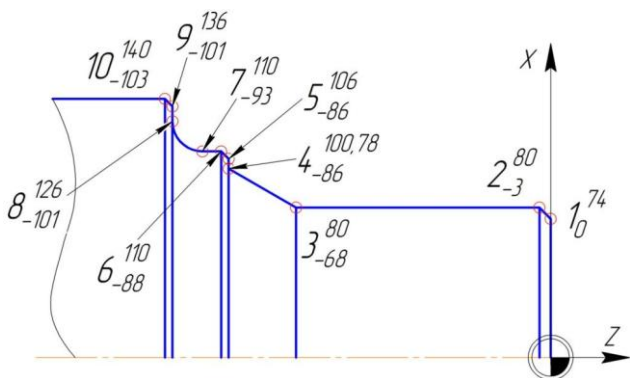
Опорні точки зовнішнього контуру деталі
